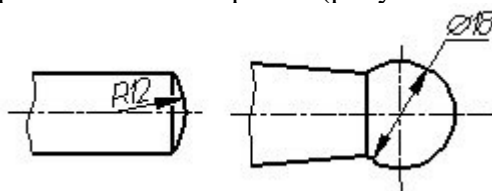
Примеры нанесения размера сферической поверхности
